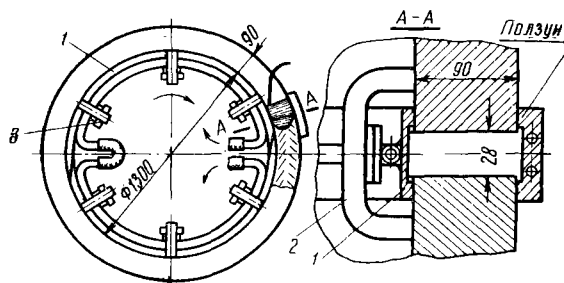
Кольцевой стык, собранный под электрошлаковую сварку
